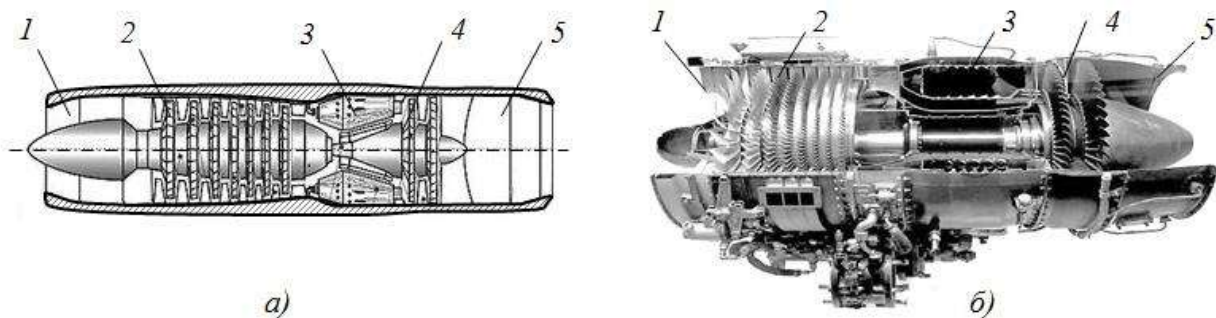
Принципова схема(а) та загальний вигляд(б) турбокомпресорного повітряного реактивного двигуна:
